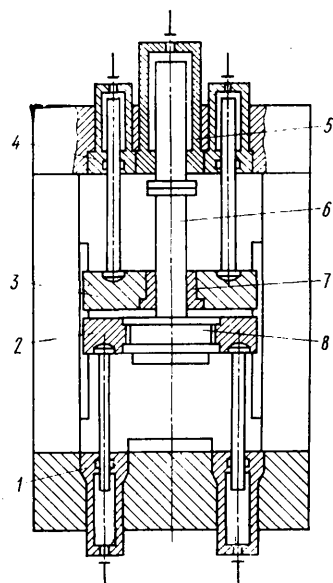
Конструктивная схема гидравлического пресса для штамповки с кручением
